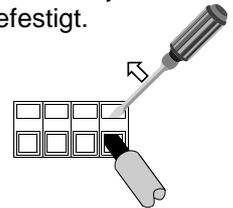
Verdrahtung mit schraubenlosen Zugfeder-Klemmen
